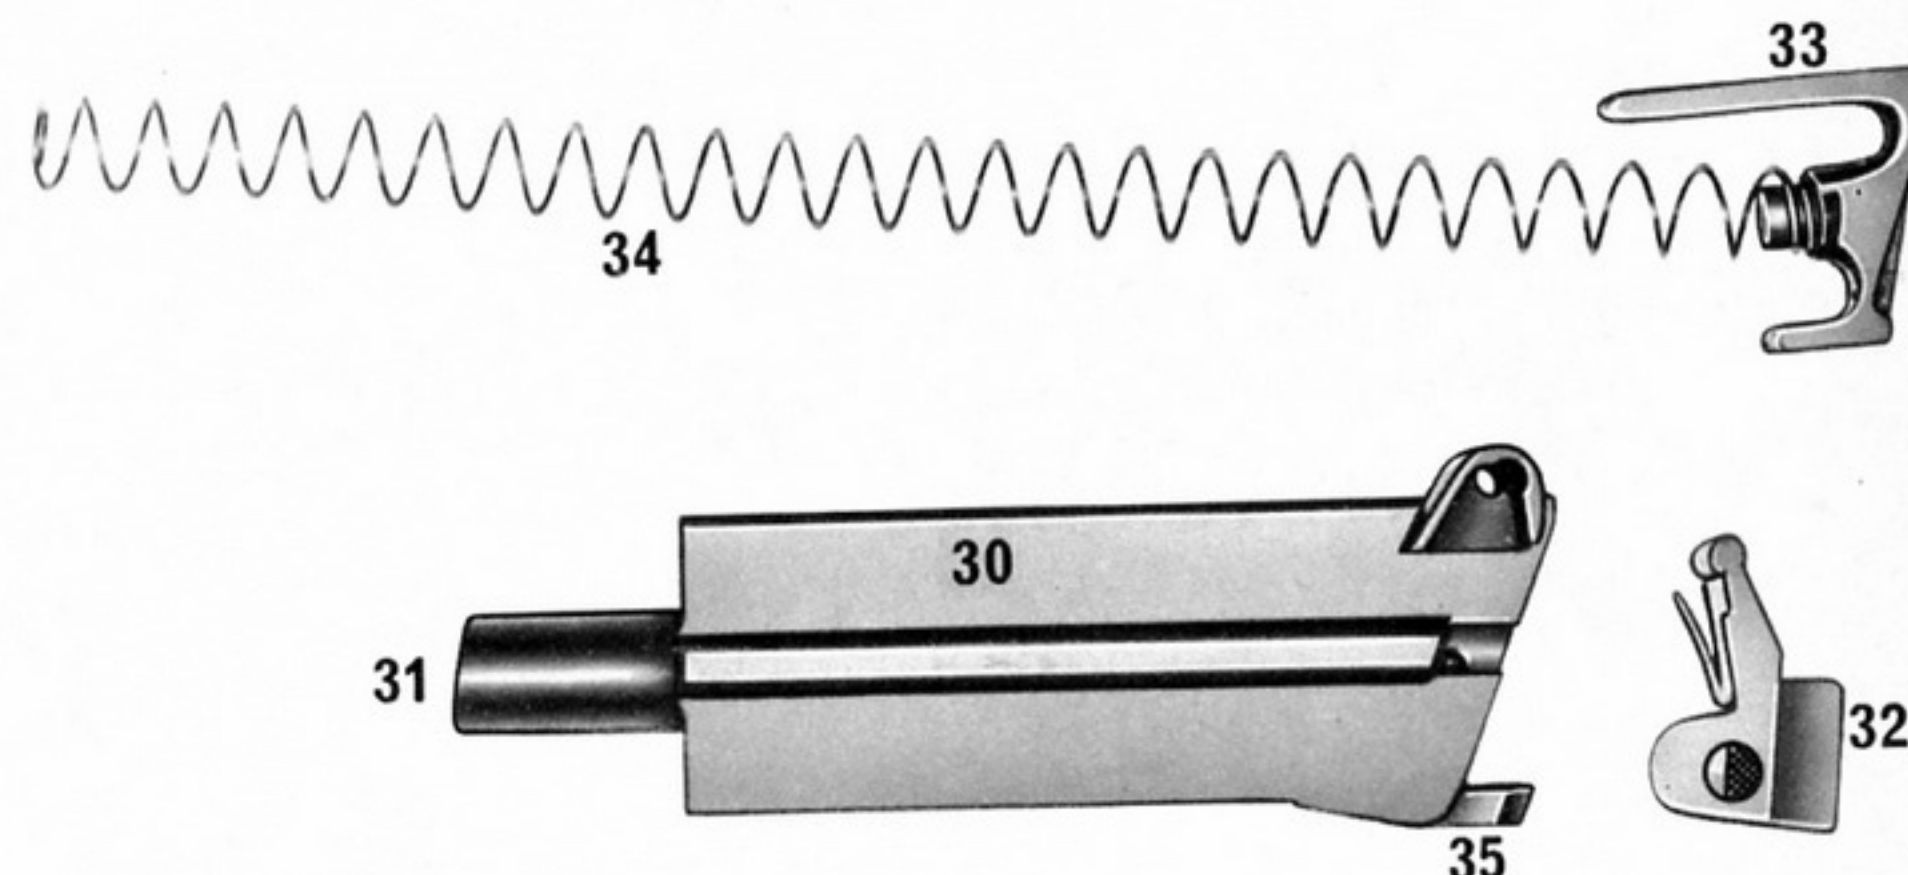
Magazin zerlegt: 31 = Magazinhülse für Zubringerfeder, 32 = Klappe, 33 = Zubringer, 34 = Zubringerfeder, 35 = Abstreifkante.
